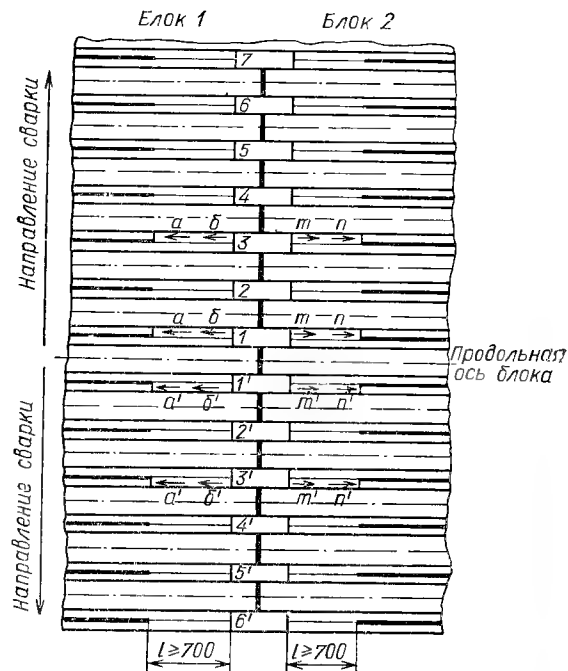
Схема сварки продольных швов по плавникам в районе стыков труб.
